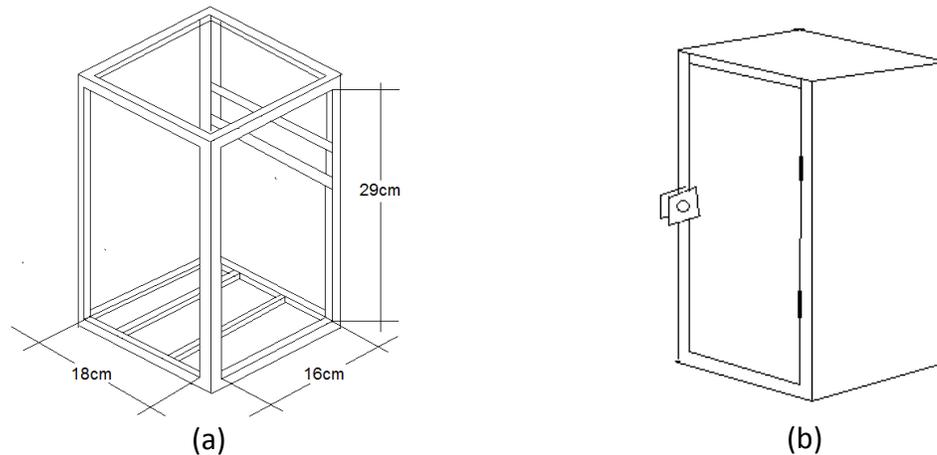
a) Dimensionamiento b) Soporte de la batería terminada.
